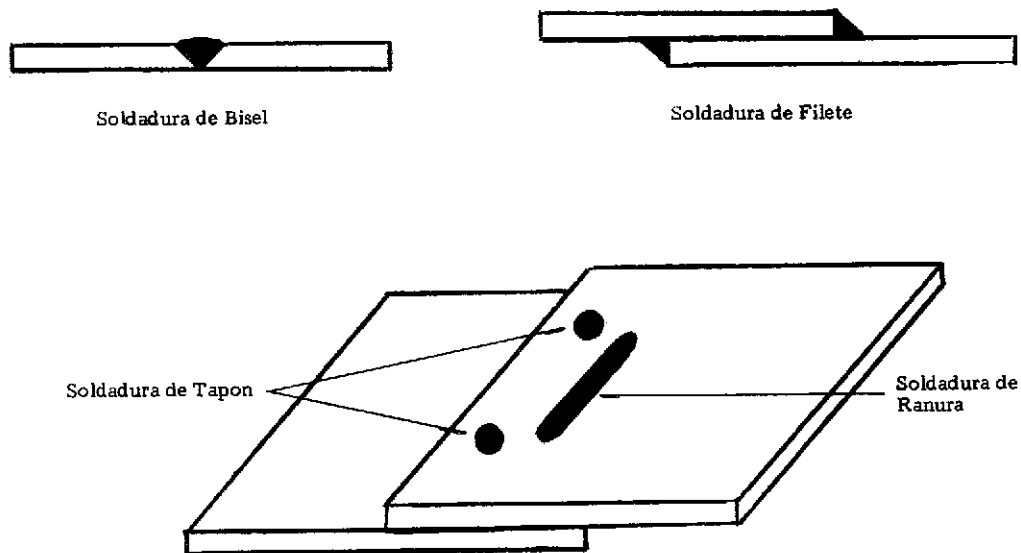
Tipos de soldaduras de unión.
